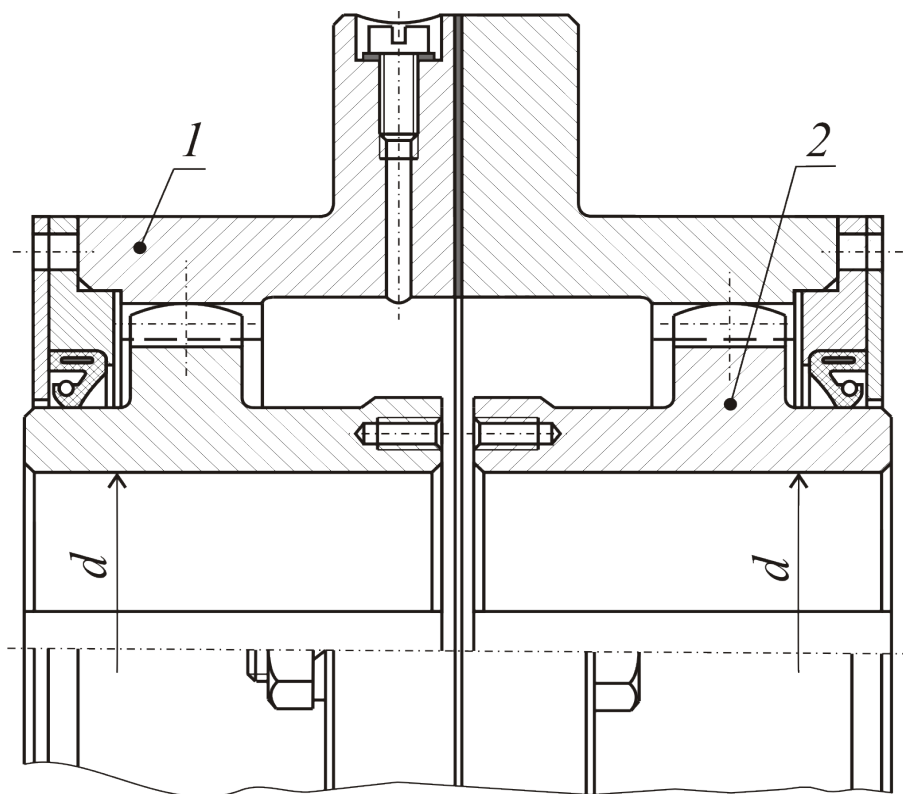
Зубчатая муфта: 1- обойма; 2- втулка
